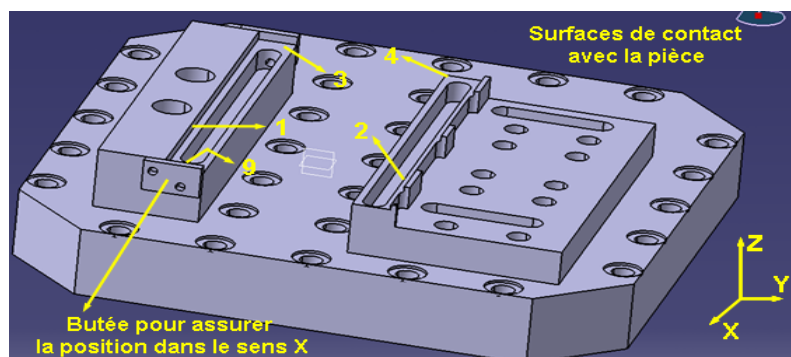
Surfaces de contact entre la pièce et le montage d'usinage en phase 10
